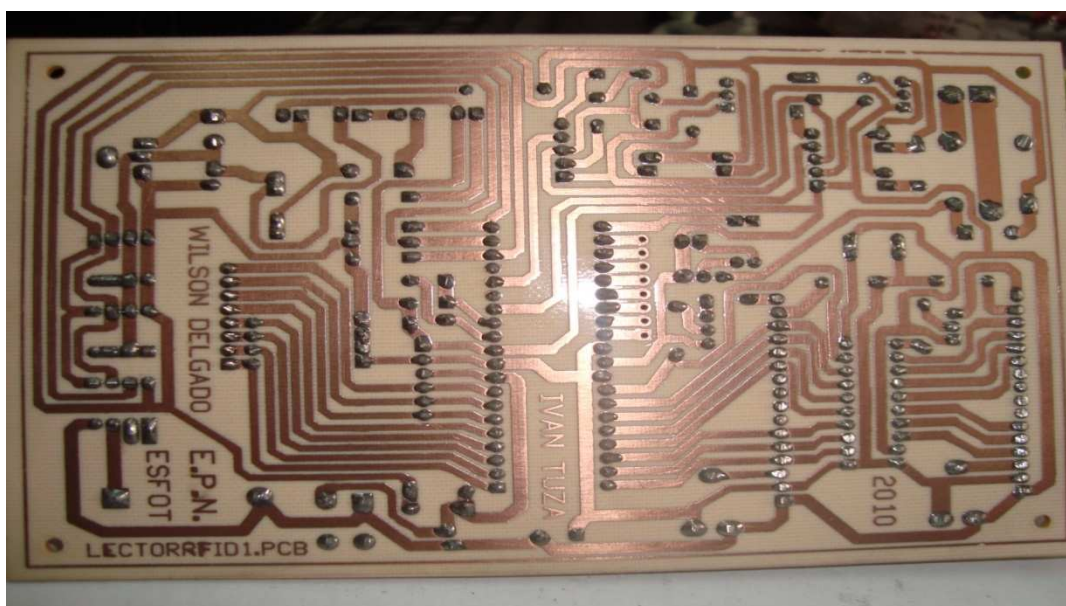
Tarjeta electrónica al final del proceso de soldadura
